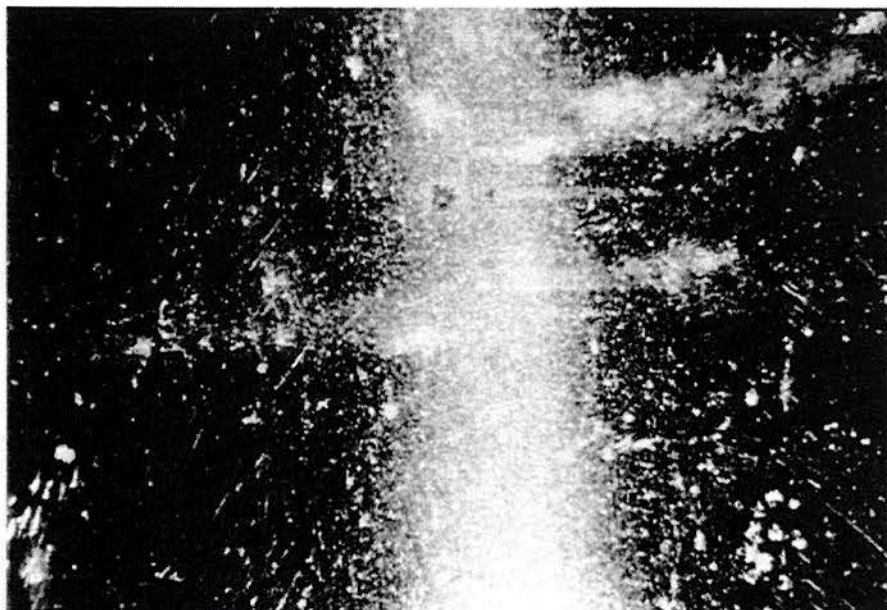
48MVT01D - pista externa LA, detalhe.
